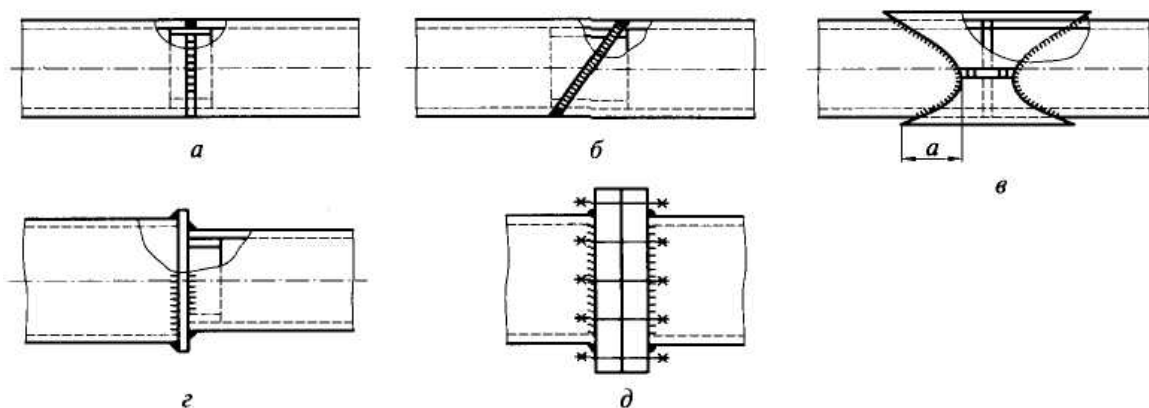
Стыковые соединения труб для изготовления опор под трубопроводы, кронштейнов, консолей или ферм:
